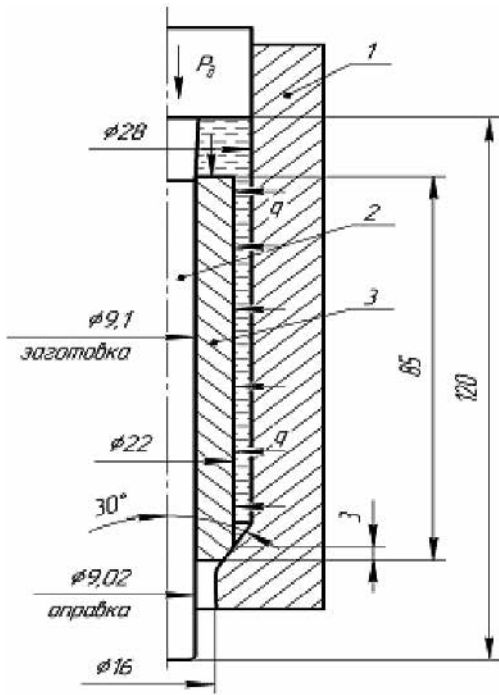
Расчётная схема гидропрессования трубчатых заготовок на оправке
